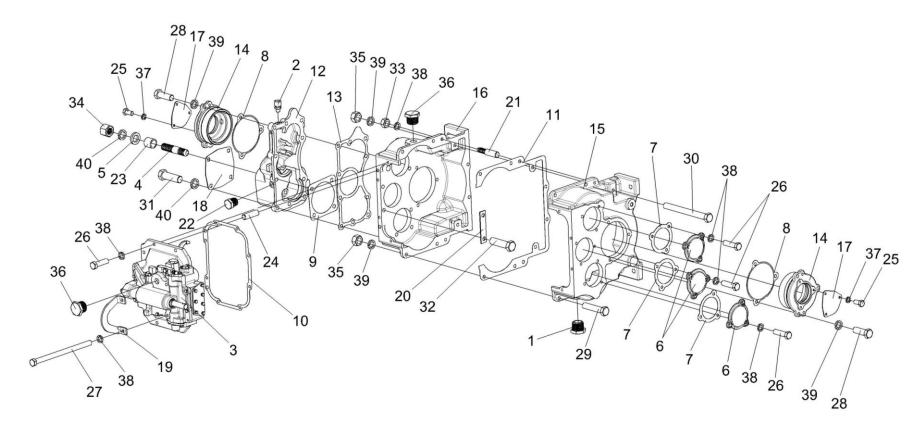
Коробка диапазонов 3518020-46150 (корпус, крышки)
